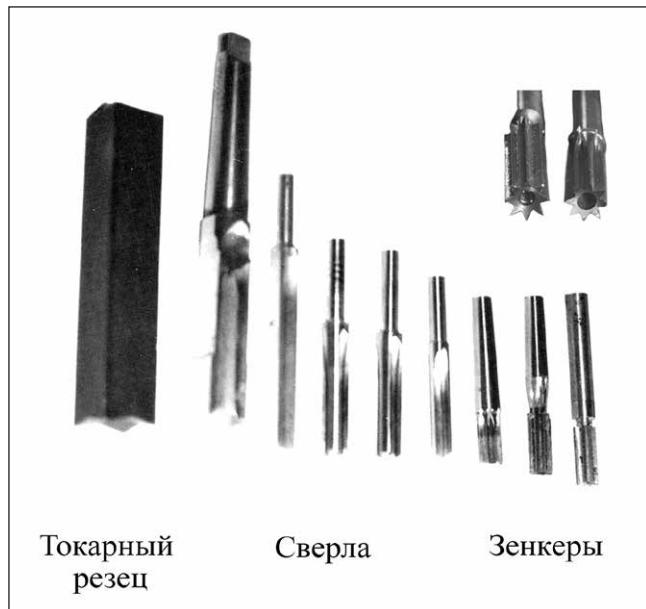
Инструменты реверсивного резания: токарный резец, свёрла, зенкеры, вверху увеличенный вид
